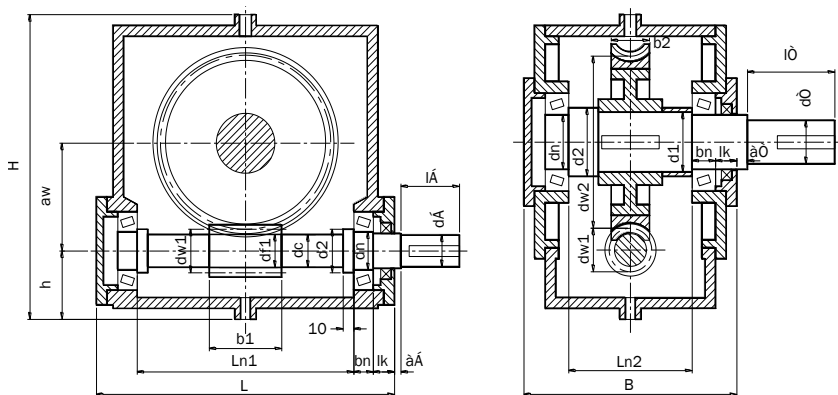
Габаритные и компоновочные размеры одноступенчатого червячного редуктора типа РЧУ по ГОСТ135683-6. К заданиям №№9 6...10.
